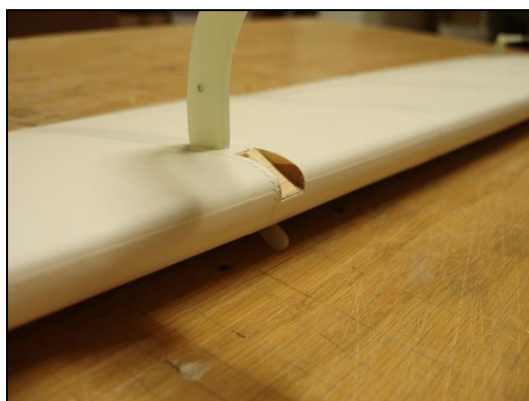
zeigt das fertig eingebaute Servo mit dem Befestigungsbrett (21).
